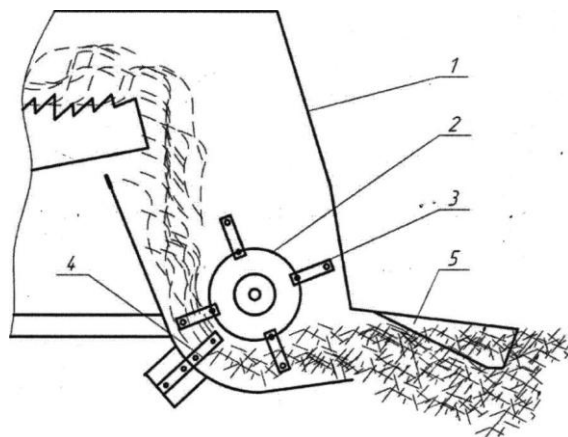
Технологическая схема измельчителя соломы зерноуборочного комбайна: 1 - корпус измельчителя; 2 - измельчающий барабан; 3 - нож измельчающего барабана; 4 - противорезущее устройство; 5 - разбрасыватель
